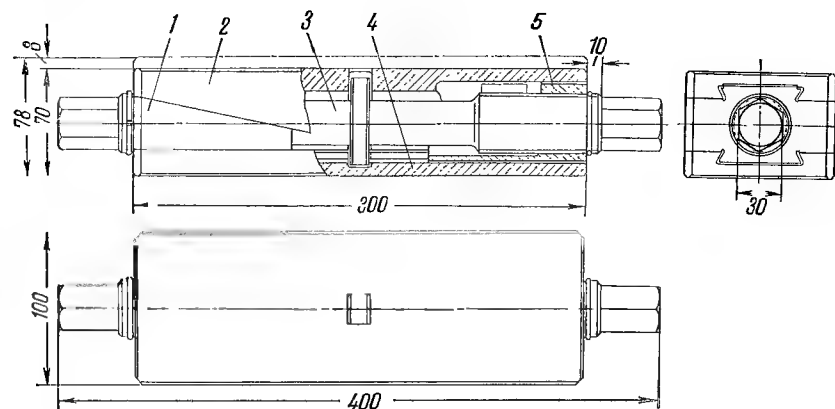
Клиновой домкрат для выверки фундаментных рам.
